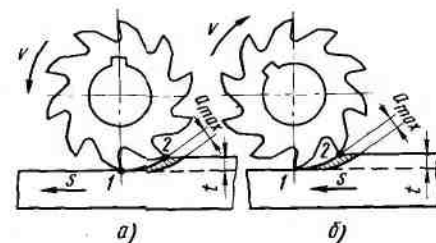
Схемы встречного (а) и попутного (б) фрезерования
